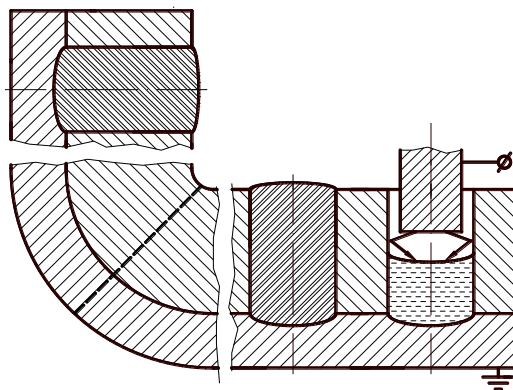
Зчеплення пластин зігнутої заготовки з біметалу на другому його краї.
